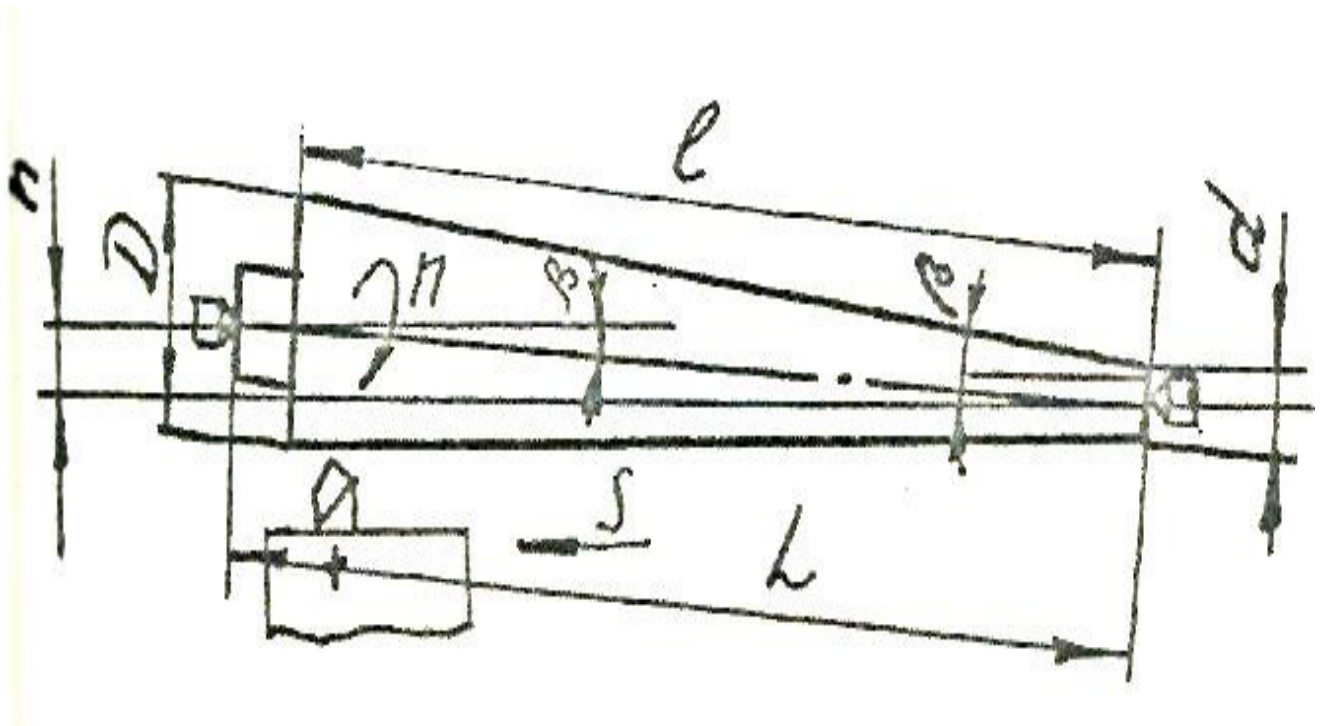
Схема обработки конической поверхности поворотом верхних салазок
